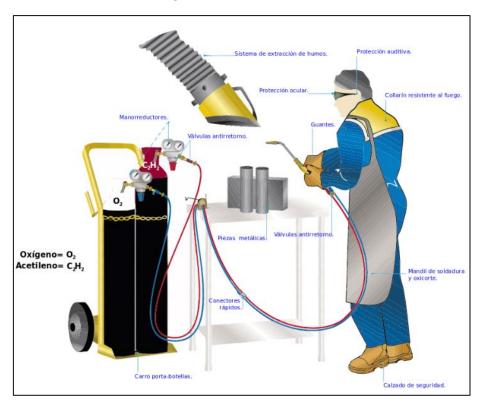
Estación correcta y segura para soldadura y oxicorte con soplete de gas.
